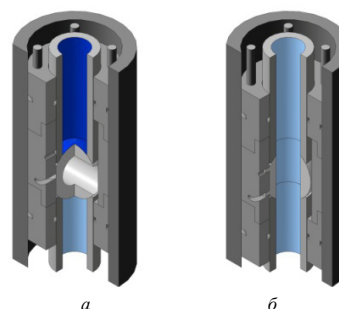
3D-модель исполнительного механизма (шарового типа) клапана-отсекателя из состава МКЗП: а – закрытое положение; б – открытое положение
